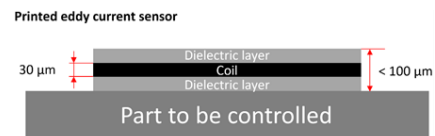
Capteur de courants de Foucault imprimé, dimensions typiques
